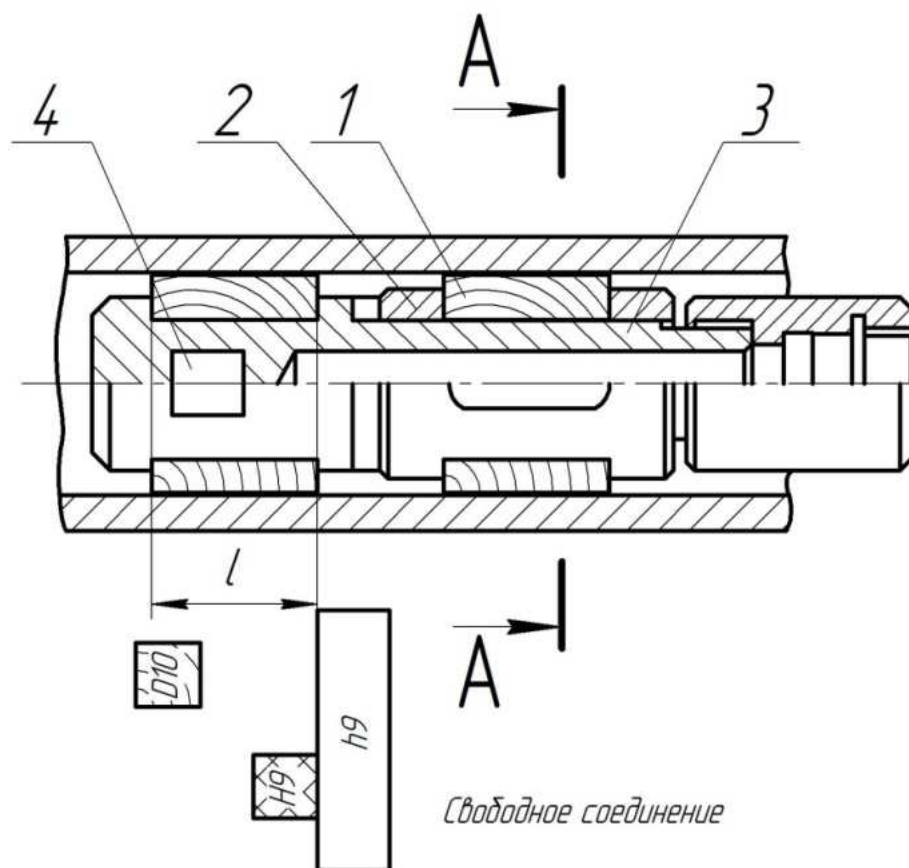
Схема центрирования расточной головки направляющими при свободном или нормальном соединении с пазами по их длине: 1- направляющая, 2- втулка; 3- корпус борштанги расточного станка; 4 - расточной резец
